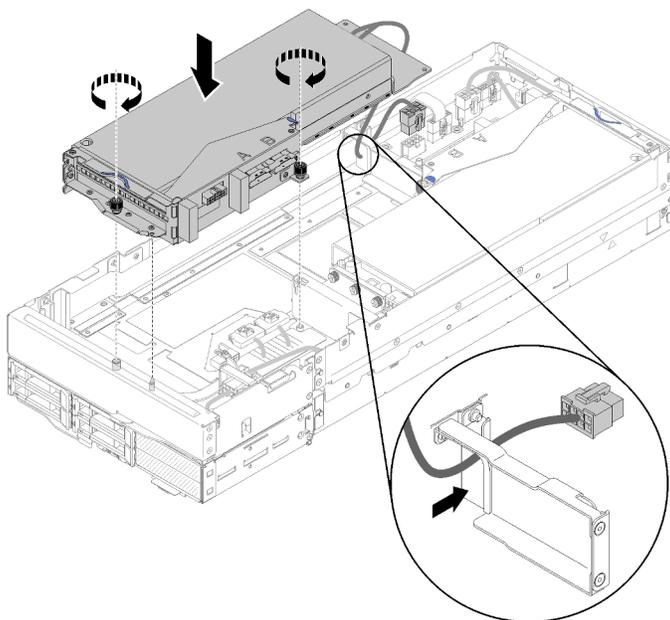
Instalando o conjunto de placa riser frontal no nó de expansão
